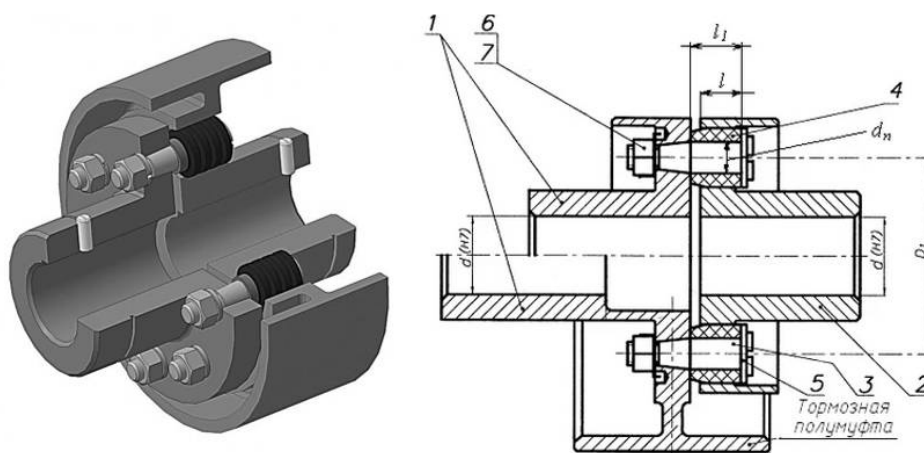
Модель (слева) и чертеж (справа) муфты упругой втулочно-пальцевой: 1, 2 – полумуфты; 3 – палец; 4 – втулка упругая; 5 – шайба для пальцев; 6 – шайба стопорная с носком; 7 – гайка
